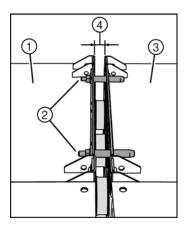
Parafusos de fixação de guiamento dispostos na chapa de fixação
